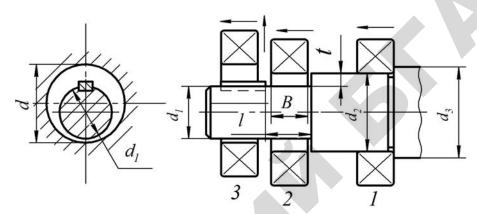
Демонтаж подшипника без снятия шпонки
